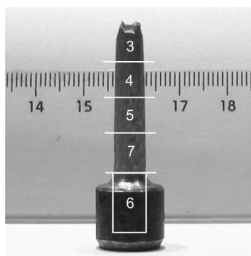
Разрушившийся при продольном растяжении образец стали Ст3 со схемой нарезки образцов для испытаний
